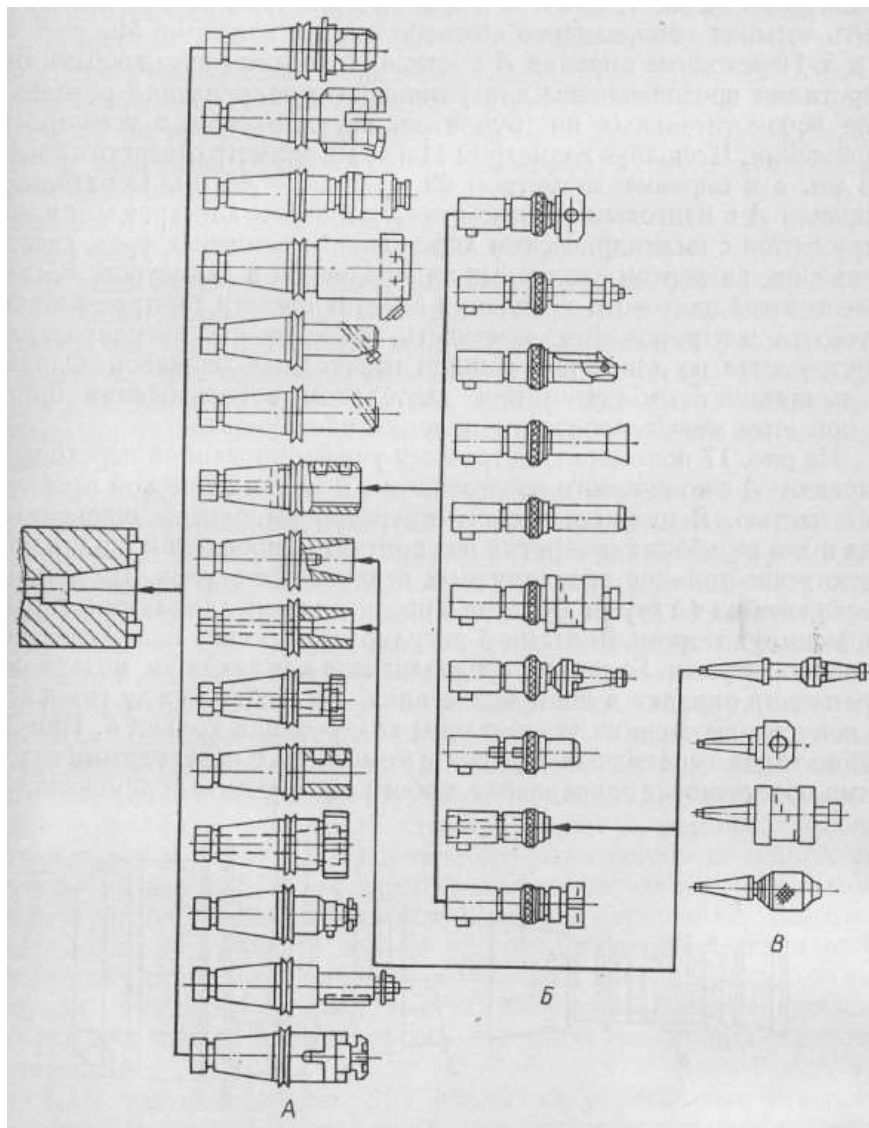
Система інструментального оснащення для верстатів з ЧПК .
